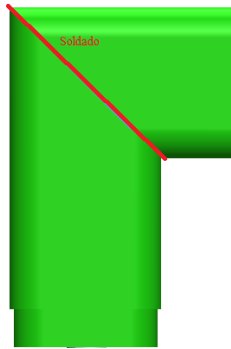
Vistas de soldado pieza N°2 (Fuente 86)
